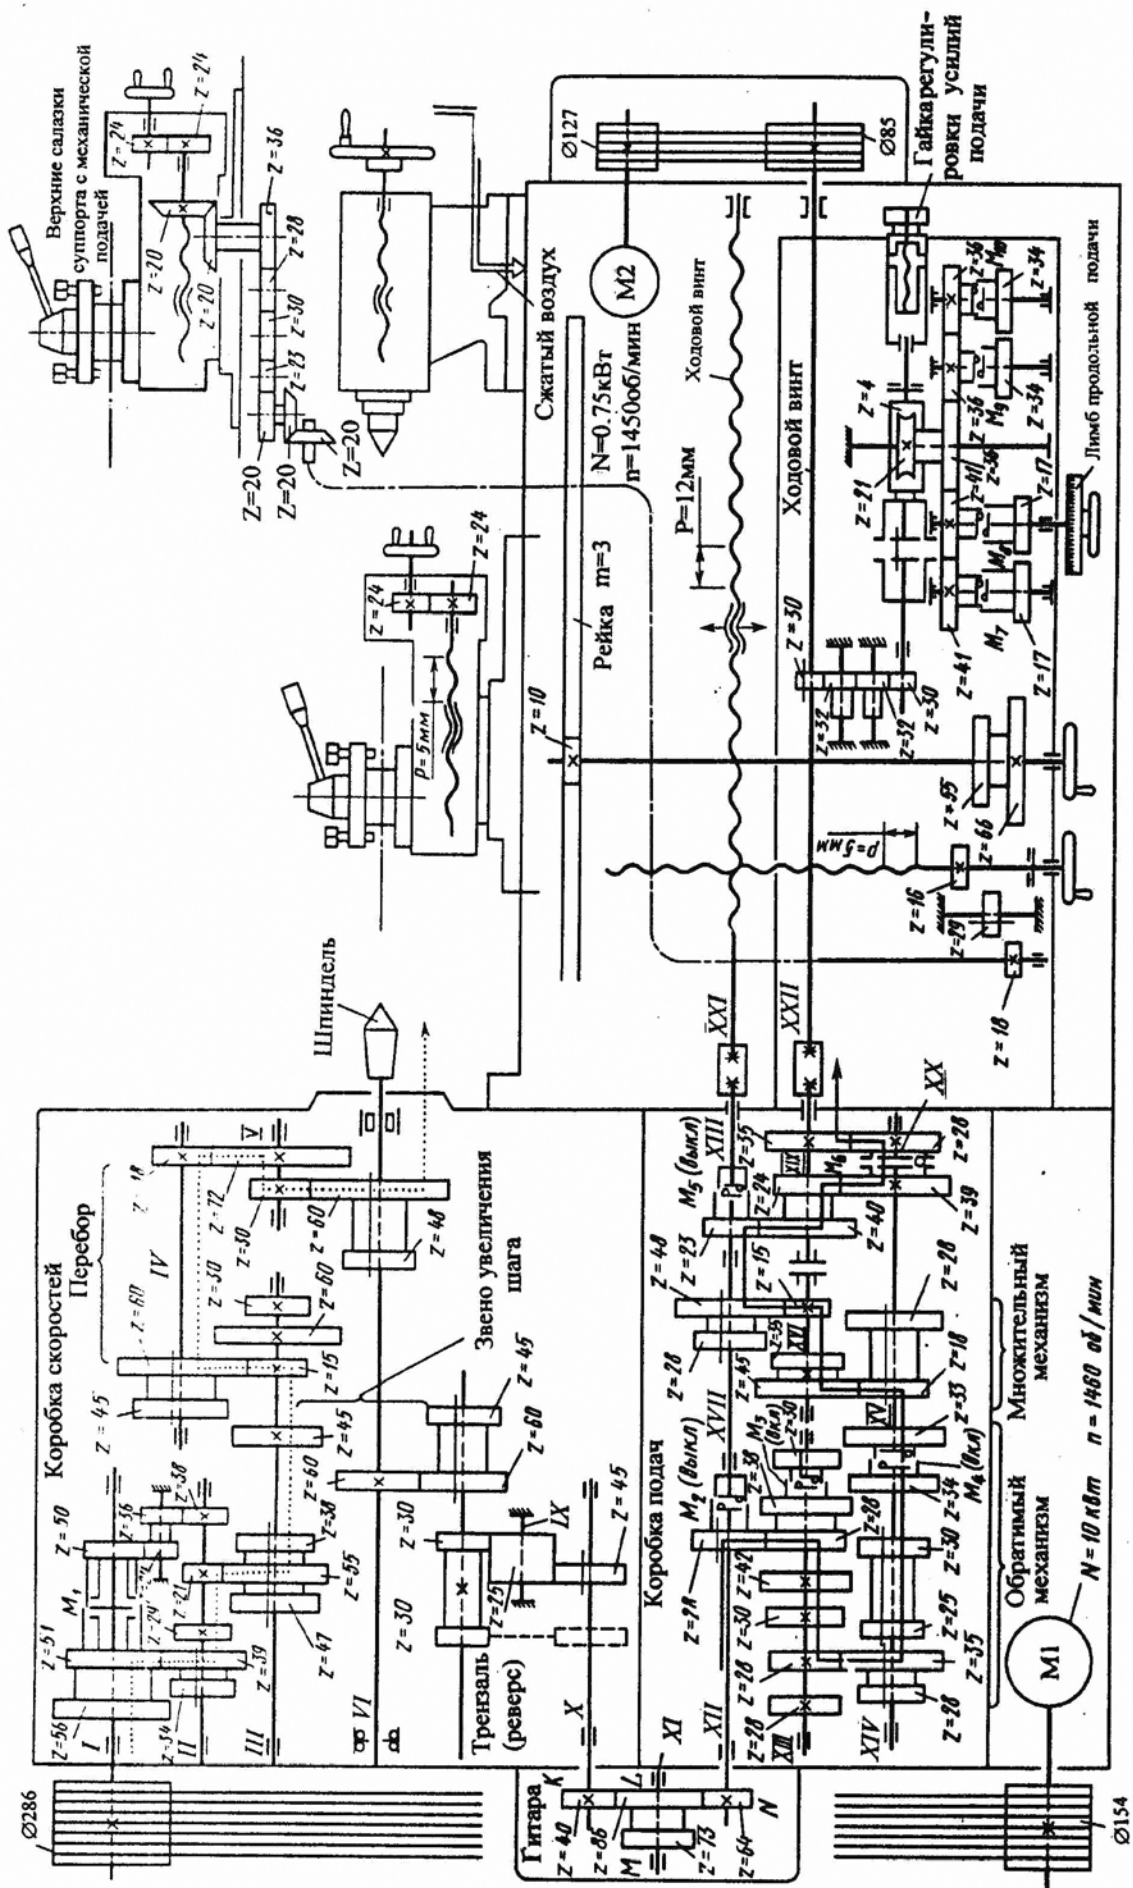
Кинематическая схема токарно-винторезного станка модели
